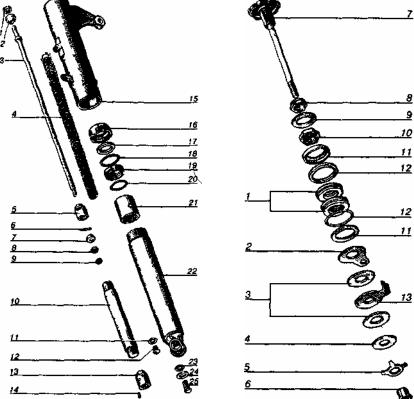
Амортизатор передней вилки мотоциклов "Днепр-11/16": 1,9- гайки; 2- наконечник; 3- шток амортизатора; 4- пружина; 5- гайка трубки; 6- штифт; 7- поршень амортизатора; 8- направляющая; 10- трубка корпуса; II- прокладка; 12- винт; 13- конус; 14- штифт; 15- кожух левый(правый); 16- гайка сальника; 17- кольцо; 18- шайба сальника; 19- манжета сальника; 20- пружина сальника; 21- корпус сальника; 22- наконечник левый(правый); 23, 24- шайбы
